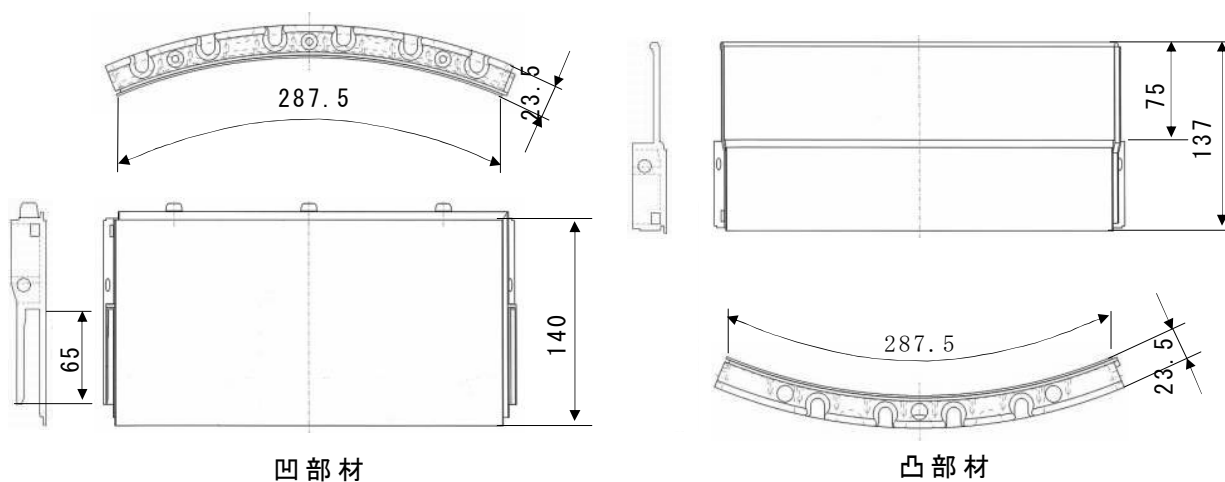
スライドタイプの形状寸法図（呼び径 800）
